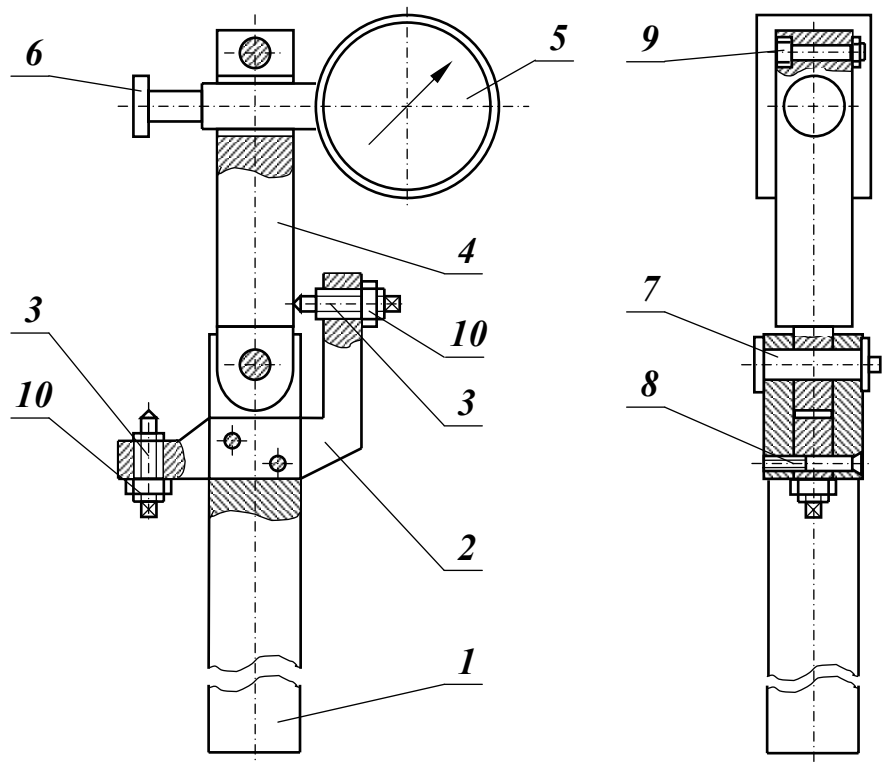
Конструктивна схема безззорного індикаторного поворотного пристрою
